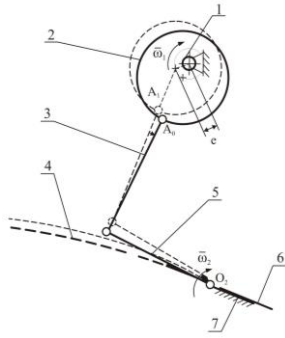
Кинематическая схема привода разрыхлителя плуга: 1 – приводной вал; 2 – эксцентрик; 3 – эксцентриковая тяга; 4 – разрыхлитель; 5 – рычаг; 6 – выкопчная скоба; 7 – башмак.
